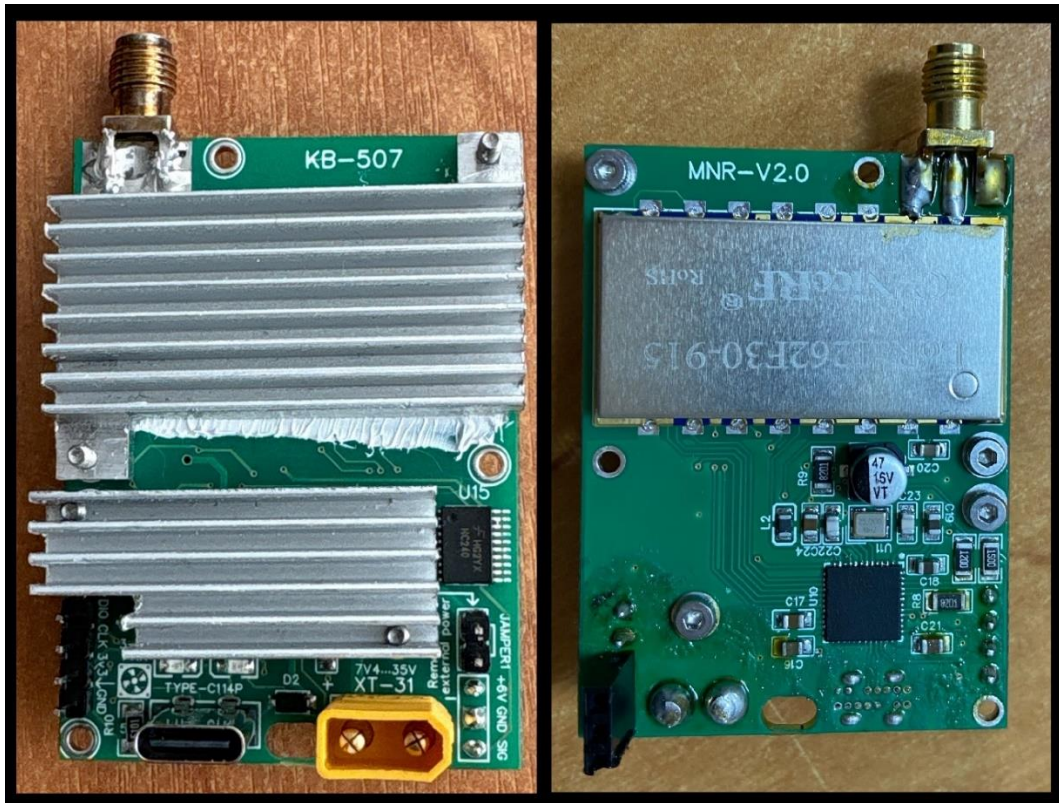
Внешний вид платы ПП Оператора после сборки.
